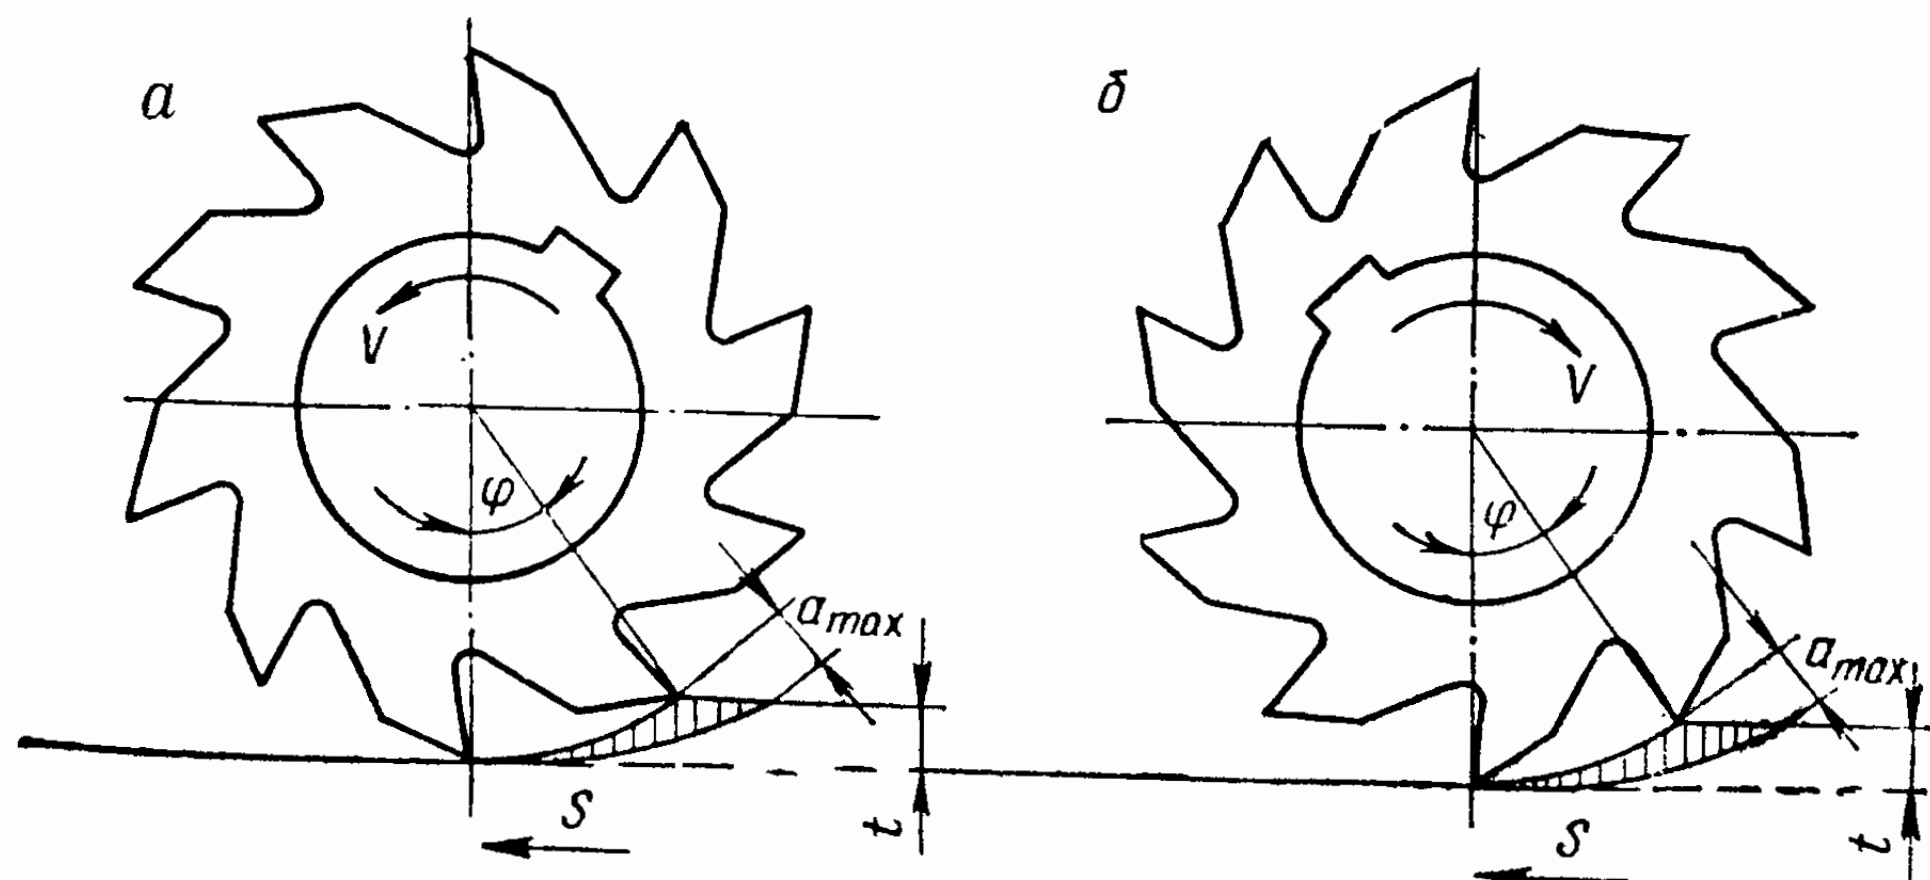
Элементы стружки при фрезеровании цилиндрическими фрезами.
